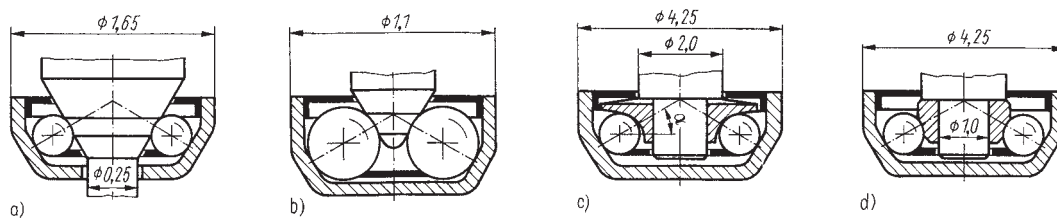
Ausführungsformen von Miniatur-Schulterkugellagern
